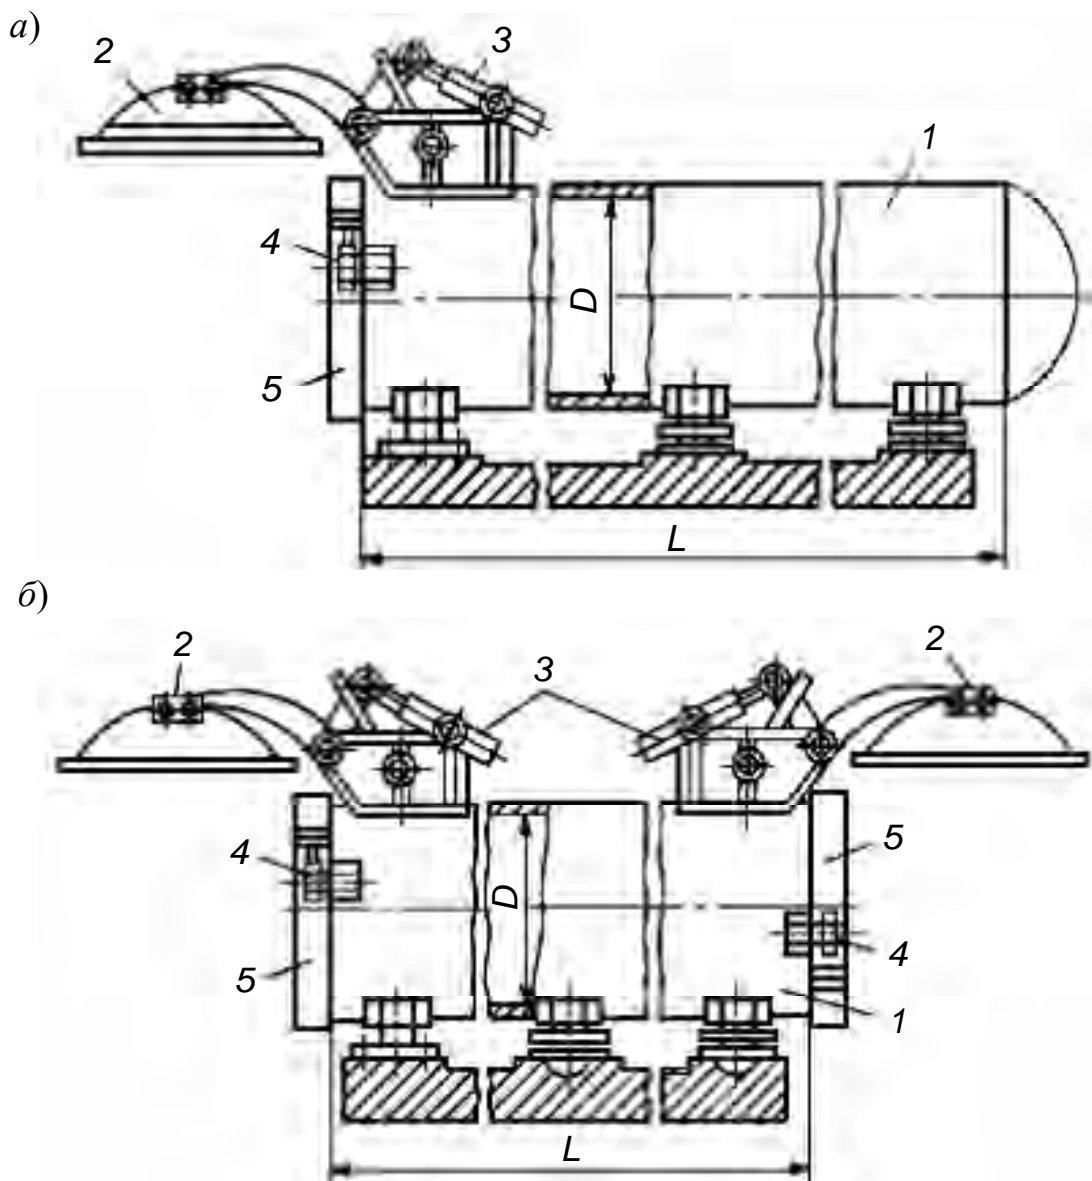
Устройство горизонтального автоклава: *a* – тупиковый автоклав; *б* – проходной автоклав; *1* – корпус автоклава; *2* – крышка; *3* – гидропривод открывания-закрывания крышки; *4* – гидропривод поворота байонетного кольца; *5* – байонетное кольцо; *D* – внутренний диаметр автоклава; *L* – длина автоклава
